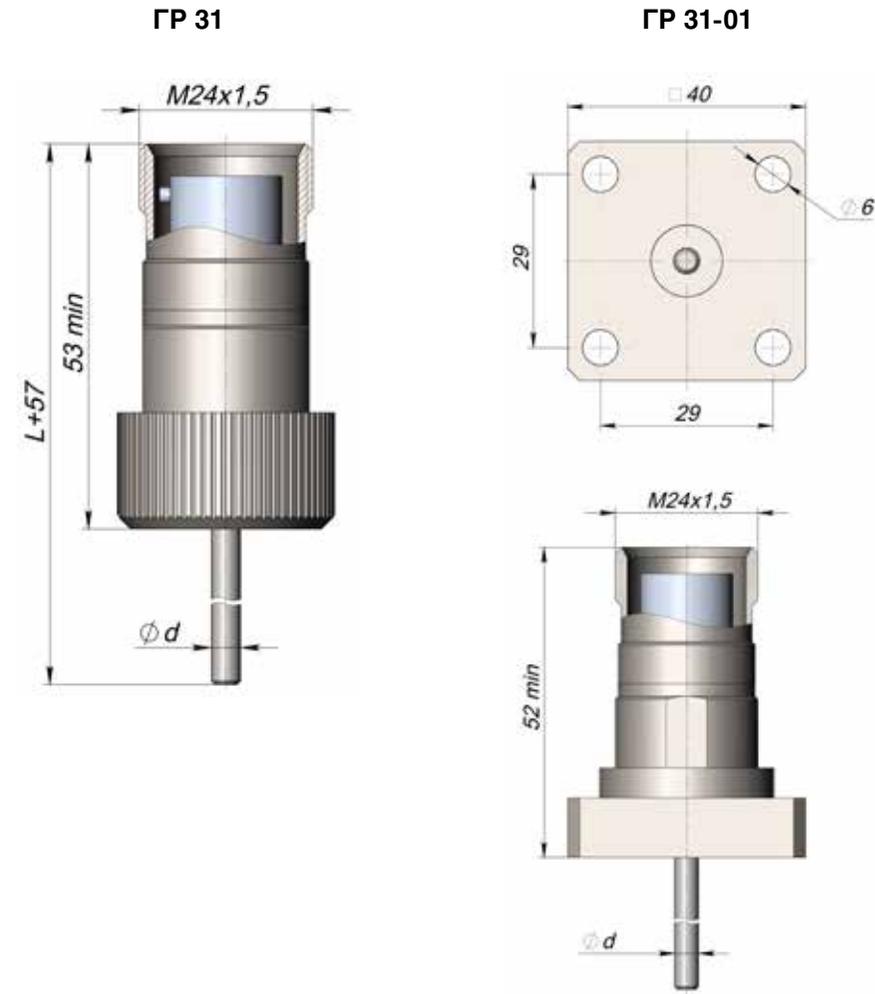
Конструкция, габаритные и присоединительные размеры.
